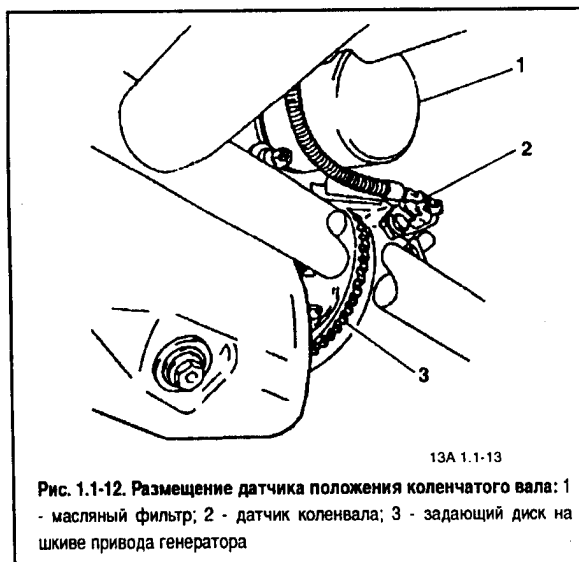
Размещение датчика положения коленчатого вала: 1 - масляный фильтр; 2 - датчик коленвала; 3 - задающий диск на шкиве привода генератора
